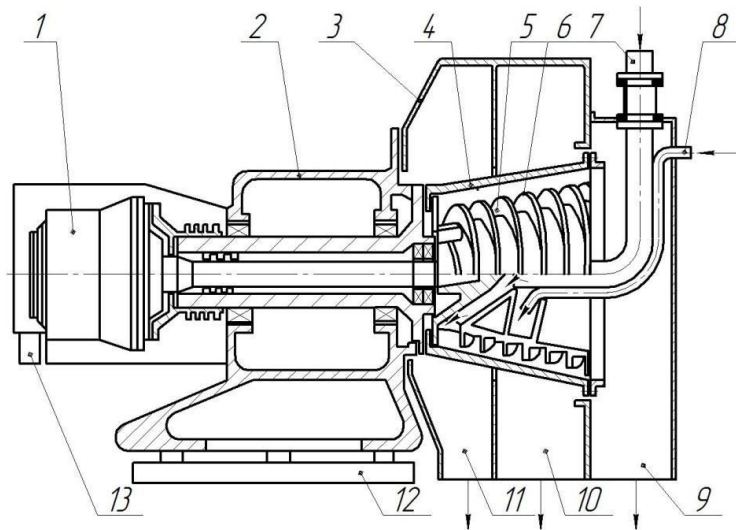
Схема фільтруючої центрифуги типу ФГШ: 1 – планетарно-дифференціальний редуктор; 2 – станина; 3 – кожух; 4 – ротор; 5 – сито; 6 – шнек; 7 – живить трубопровод; 8 – промивний трубопровід; 9 – камера для осадка; 10 – камера промывочной жидкости; 11 – камера фільтрата; 12 – виброизолирующее устройство; 13 – предохранительное устройство
